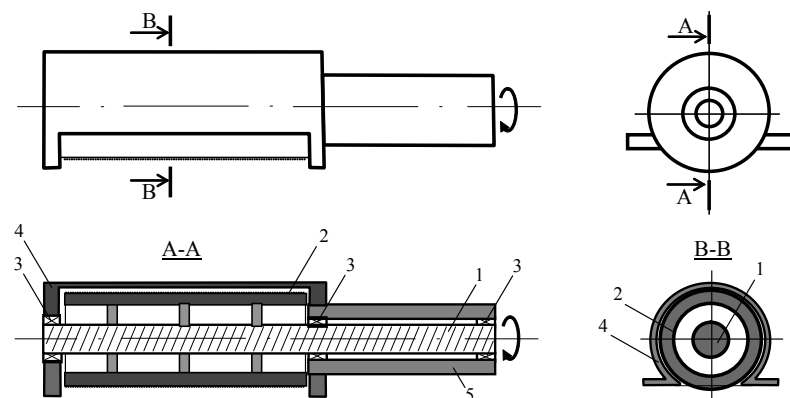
Схема ручного ротационного очистителя плодов тыквы: 1 – приводной вал; 2 – терка; 3 – подшипники; 4 – защитный кожух; 5 – ручка очистителя
